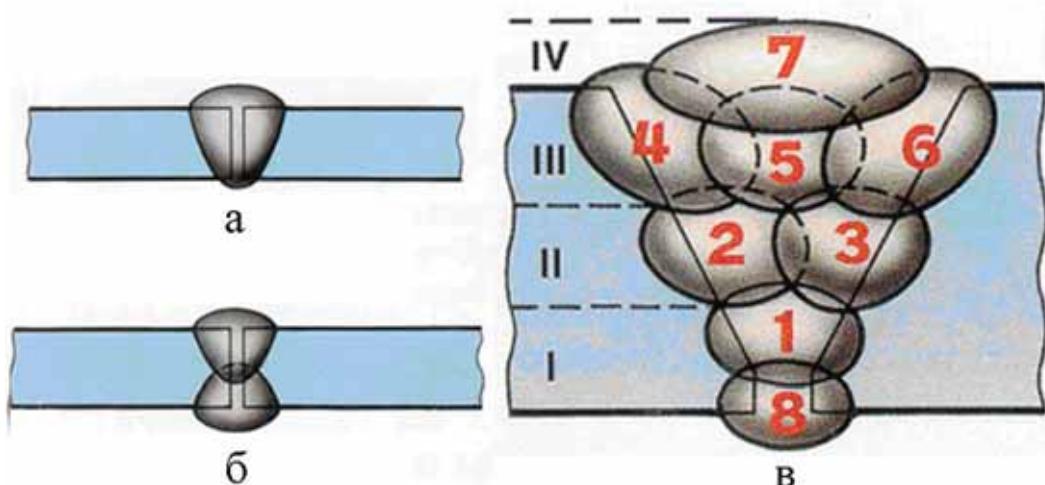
Одно- (а) и двусторонний (б) однопроходные швы и многослойный многопроходный сварной шов (в): 1–8 – очередность выполнения проходов; 1 – корневой шов; 7 – облицовочный шов; 8 – подварочный шов; I–IV – слои
